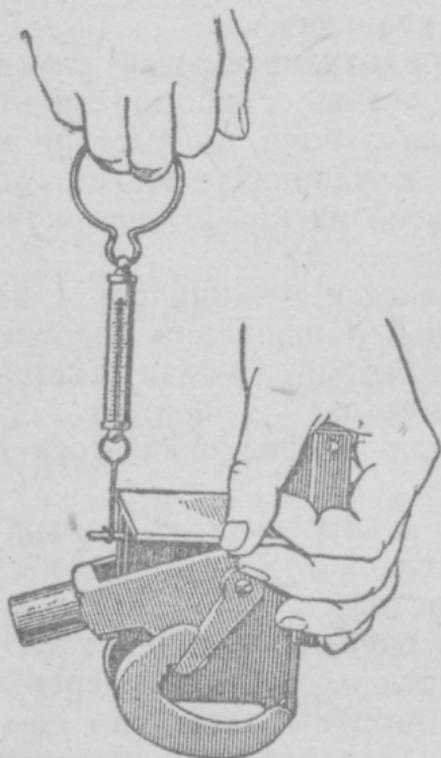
Проверка натяжения пружины верхнего спуска (весами)
